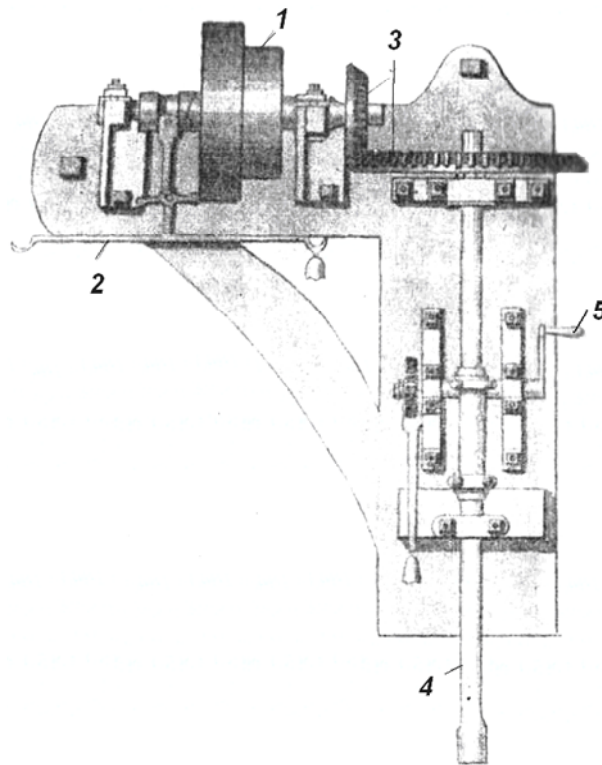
Универсальный сверлильный станок Черепановых (первая половина 19 в.)
